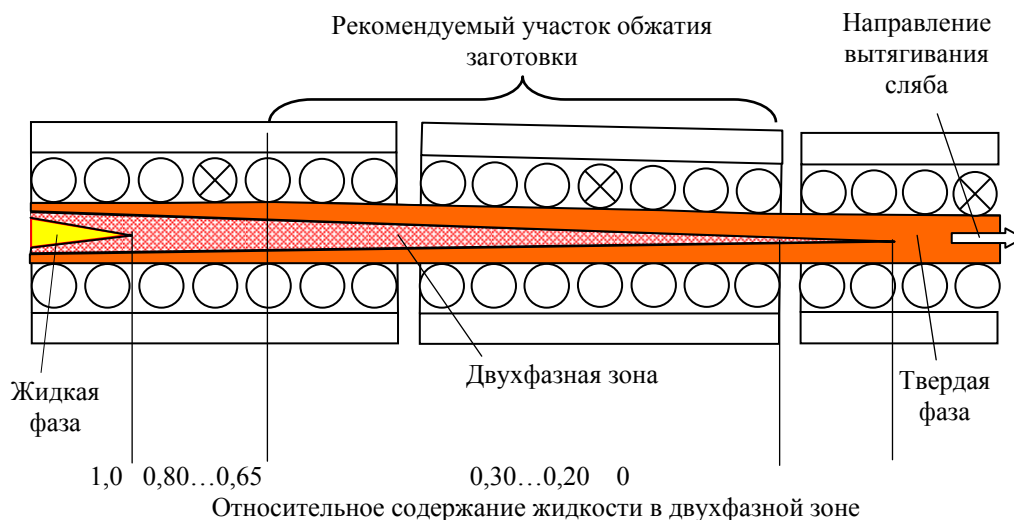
Схема мягкого обжатия слябовой непрерывнолитой заготовки в процессе разлива
